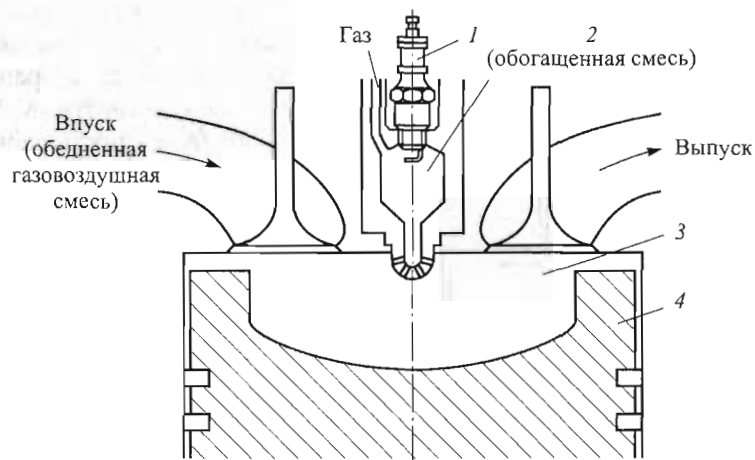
Схема предкамеры газового двигателя Atlas фирмы Ricardo:
